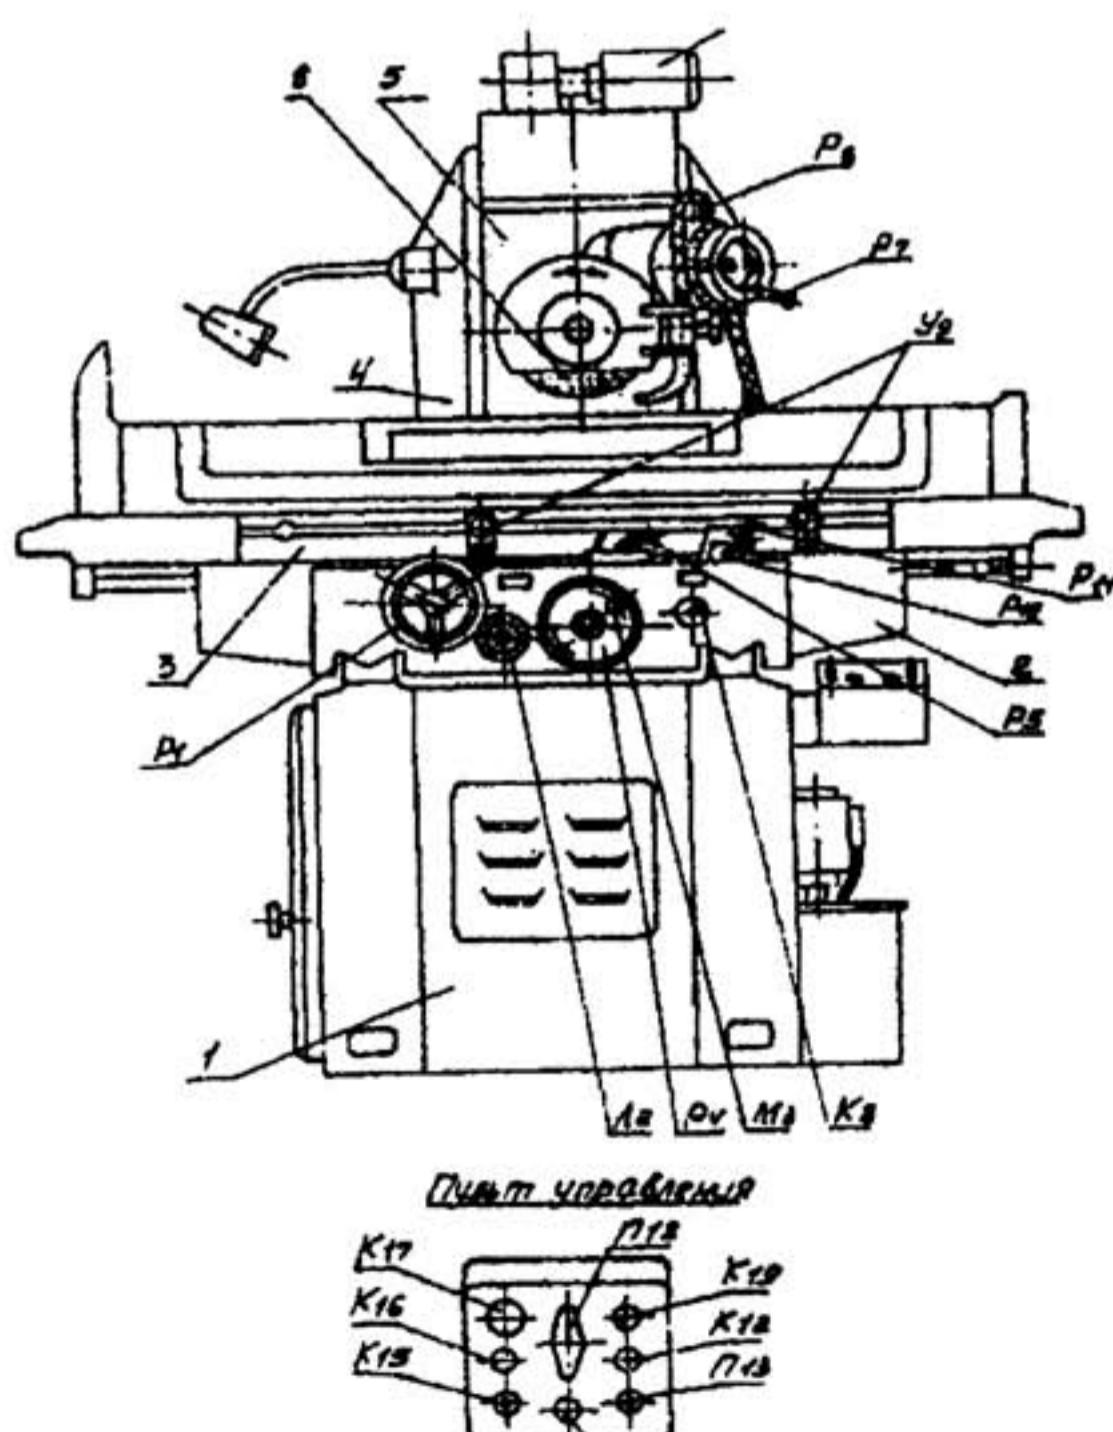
Универсальный плоскошлифовальный станок мод. ЗГ71.
